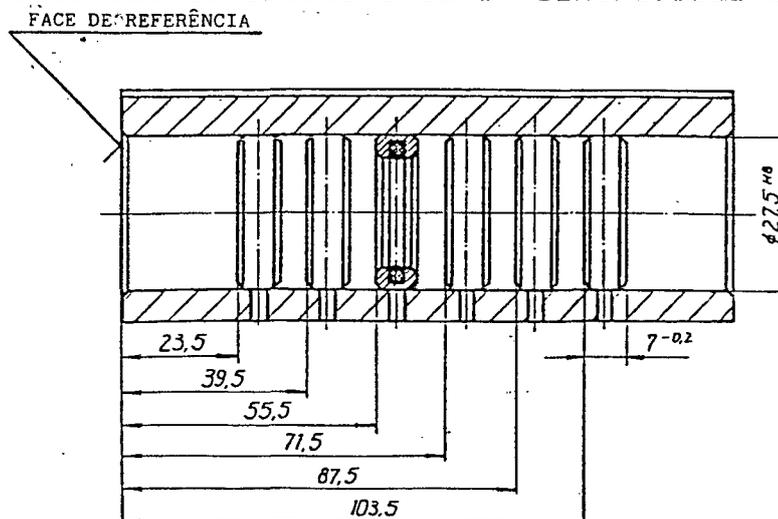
Válvula pneumática e dimensões dos afastamentos dos anéis à face de referência [54].
